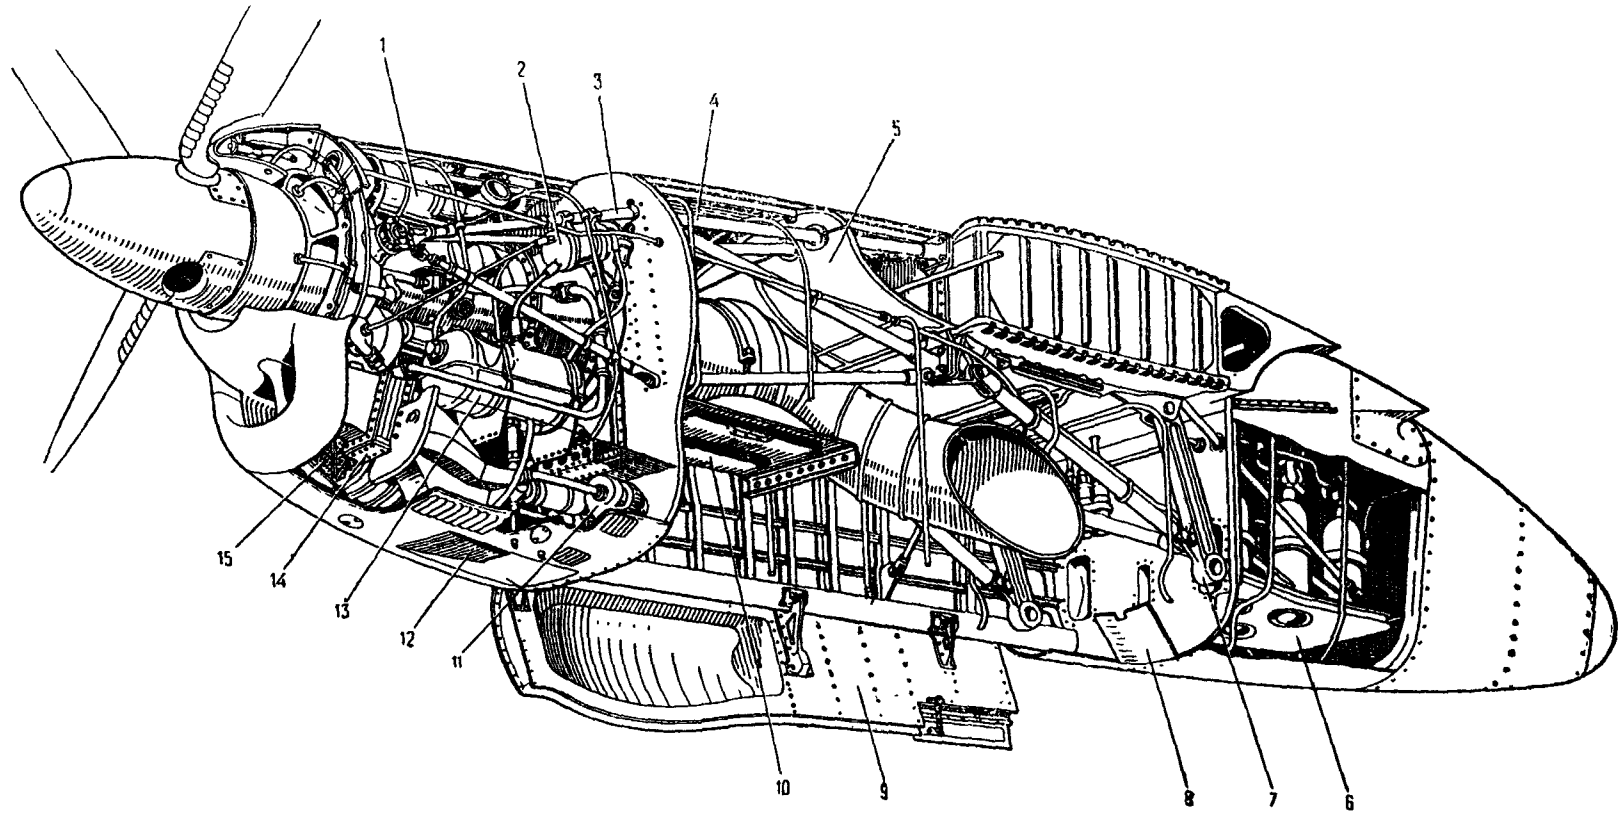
Монтаж агрегатов силовой установки с правой стороны двигателя
